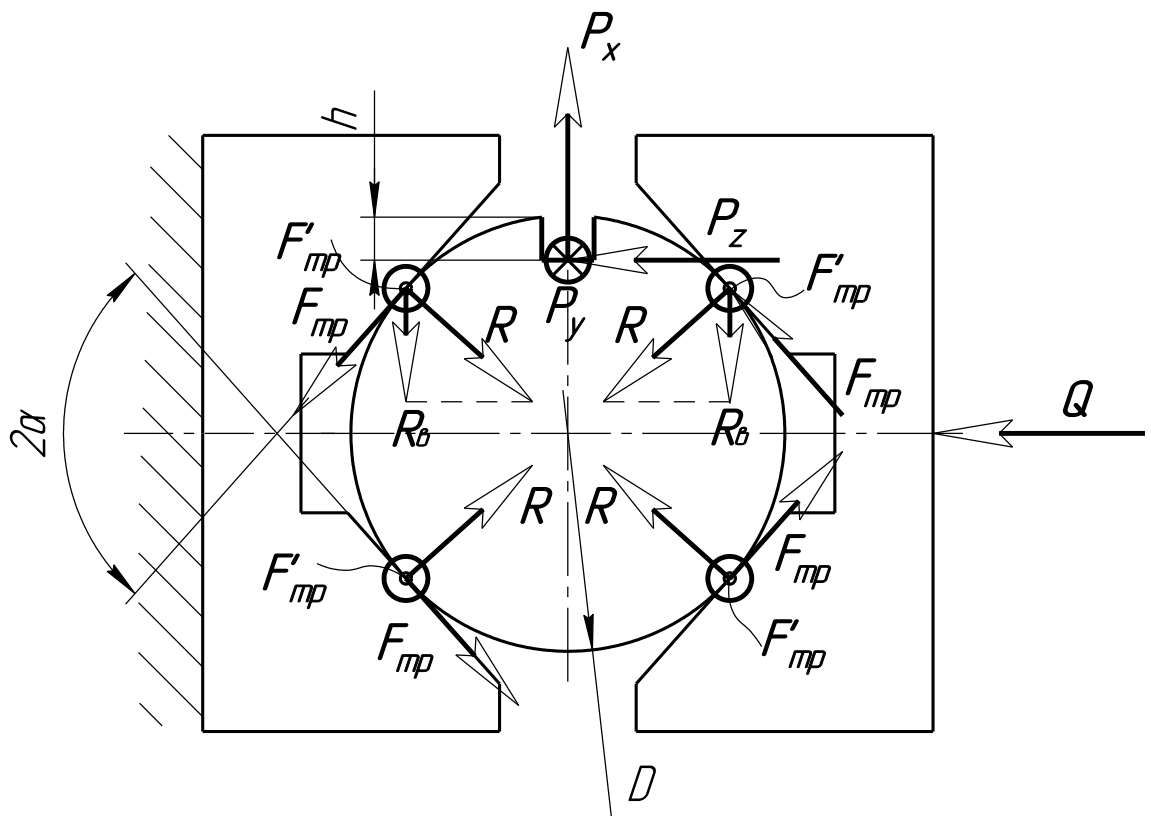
Розрахункова схема для визначення зусилля закріплення деталі при фрезеруванні шпонкового пазу кінцевою фрезою
